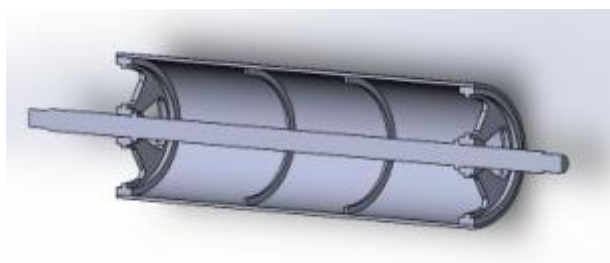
Розріз твердотільної моделі барабана базової конструкції стрічкового дозатора
